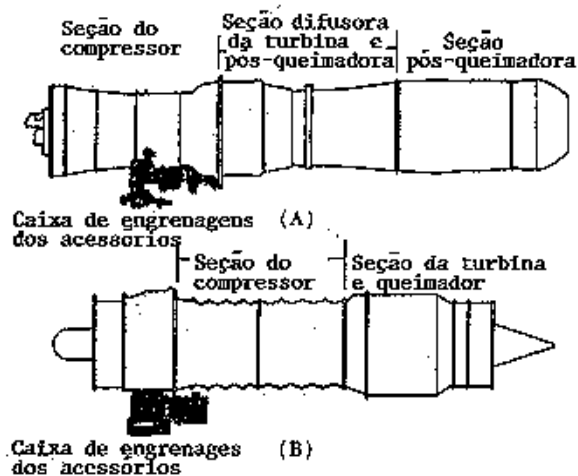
A-Caixa de engrenagens dos acessórios por baixo do compressor; e B - Caixa de engrenagens dos acessórios por baixo do suporte do rolamento dianteiro.
